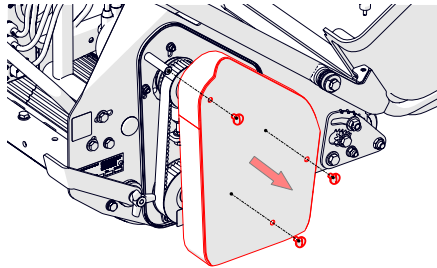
A - 3 äußere Schrauben und Abdeckung entfernen.
